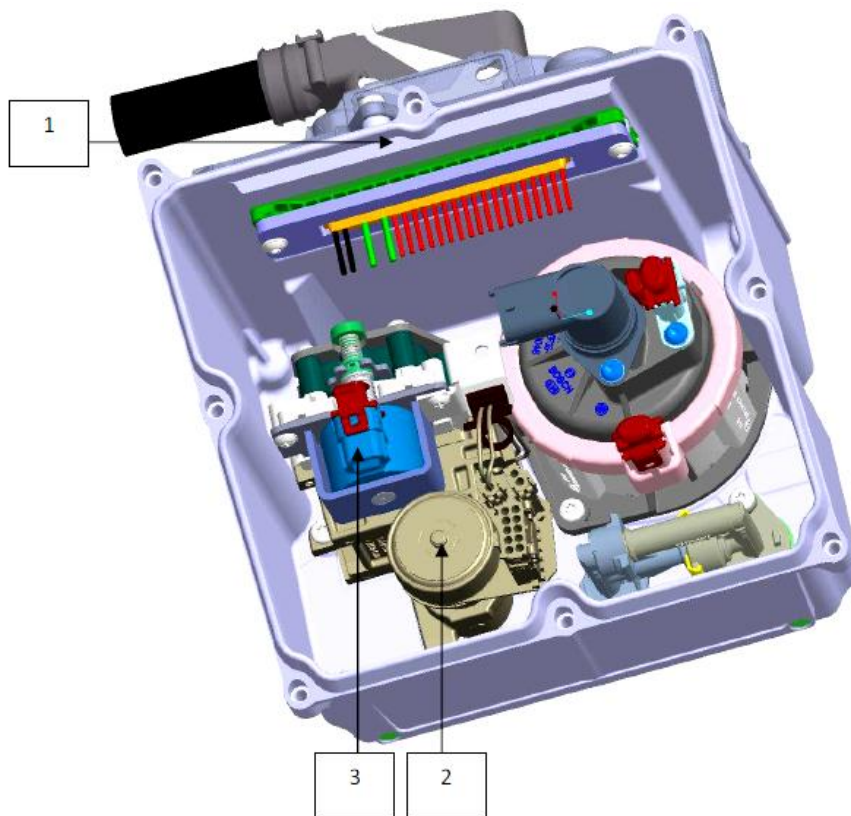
Základní části systému SCR (Mechanizace zemědělství 1/2015)
